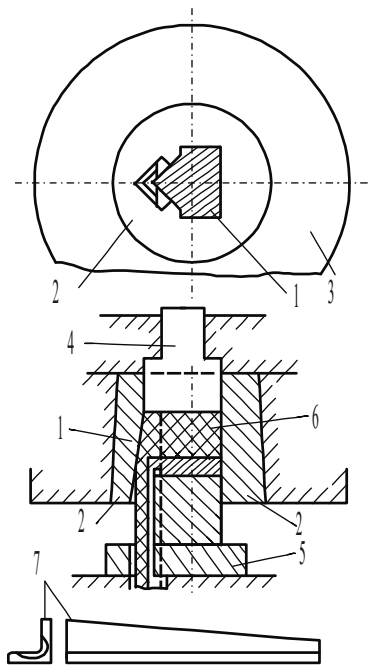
Схема зворотного пресування профілів змінного перетину: 1 – матриця; 2 – профілюючий вкладиш; 3 – корпус контейнера; 4 – виштовхувач; 5 – тримач матриці; 6 – заготовка; 7 – прес виріб.
